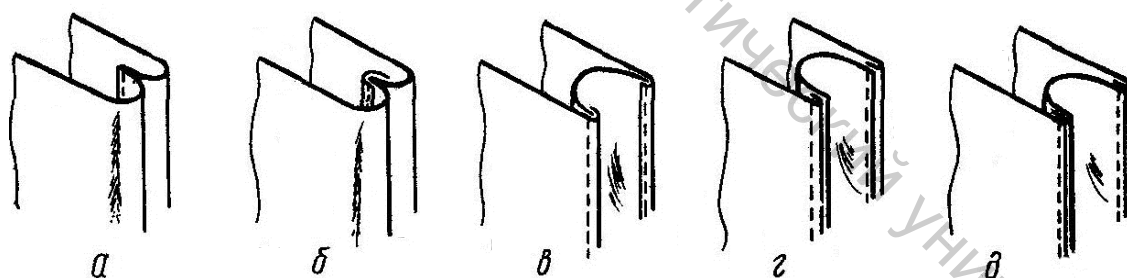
Узлы сумок, изготовленные различными способами:
